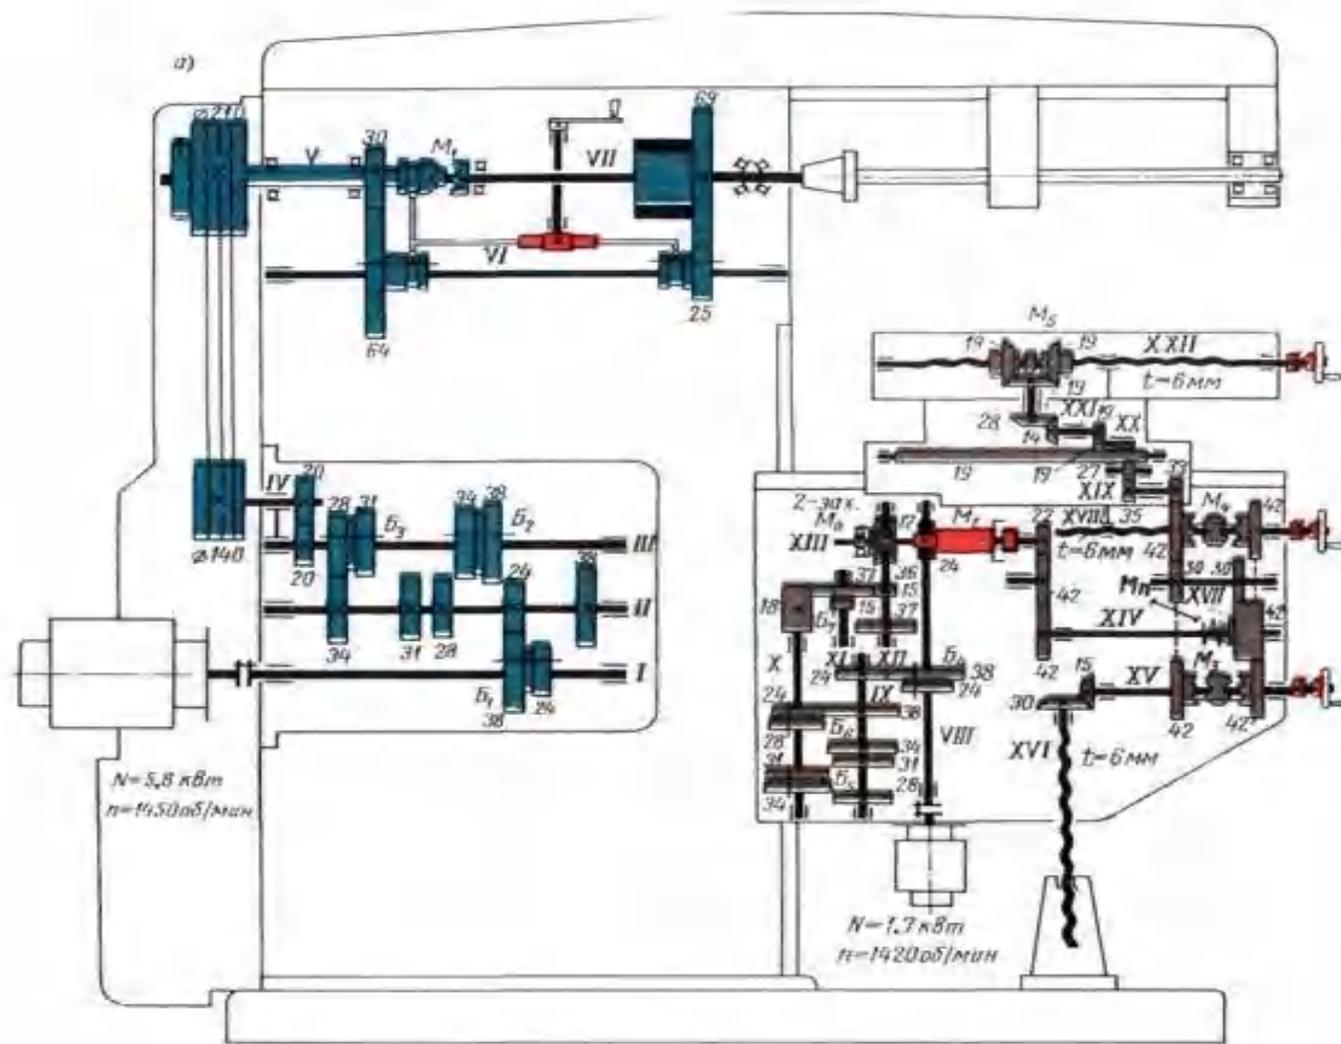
Схема кинематическая консольно-фрезерного станка 6Н81Г.
